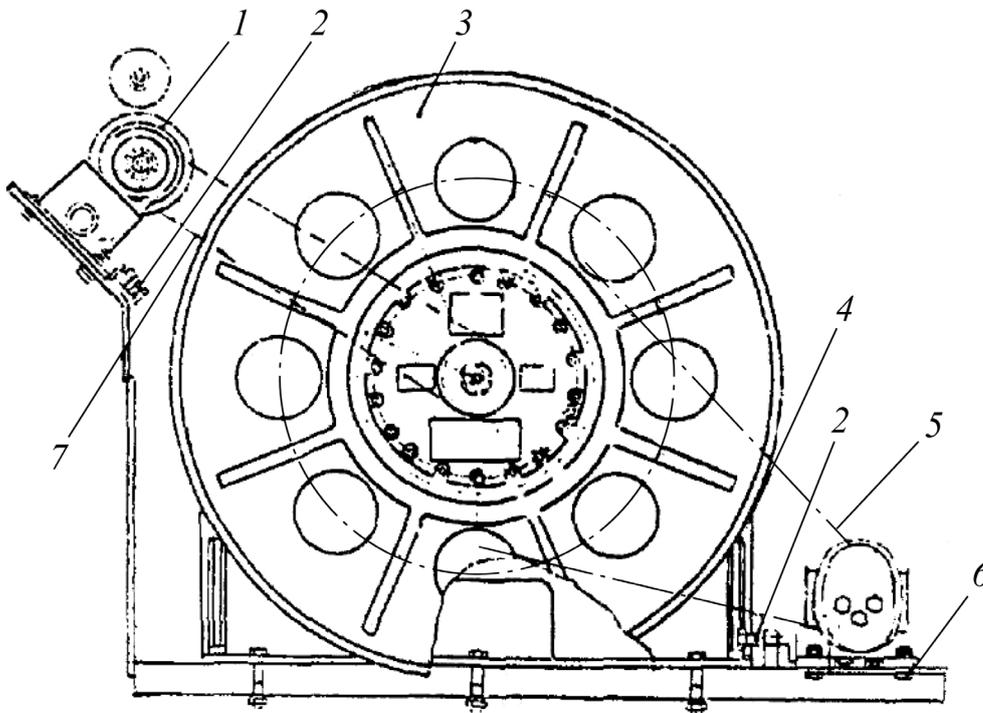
Узел кабельного барабана: 1 – кабелеукладчик; 2 – винты для натяжения цепей кабелеукладчика; 3 – барабан кабельный; 4 – кронштейн; 5 – цепь; 6 – плита; 7 – цепь кабелеукладчика
